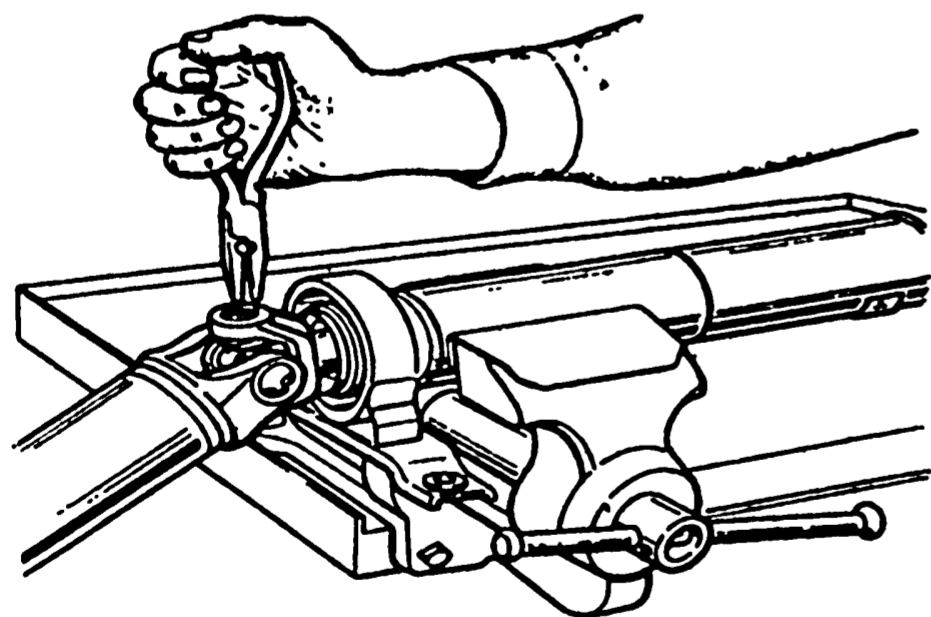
Извлечение стопорных колец подшипников крестовины
